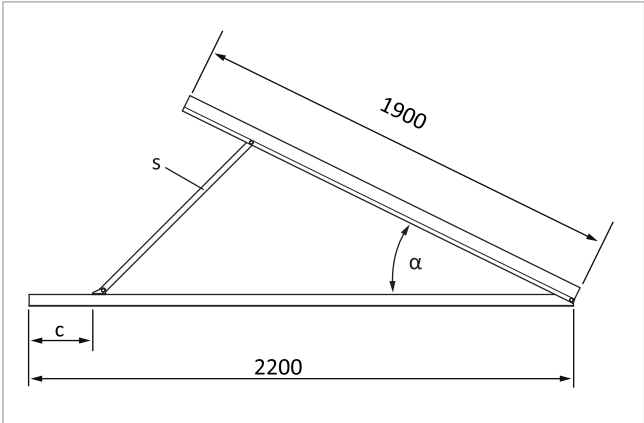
Soporte para tejado plano, dimensiones y ángulo de colocación
